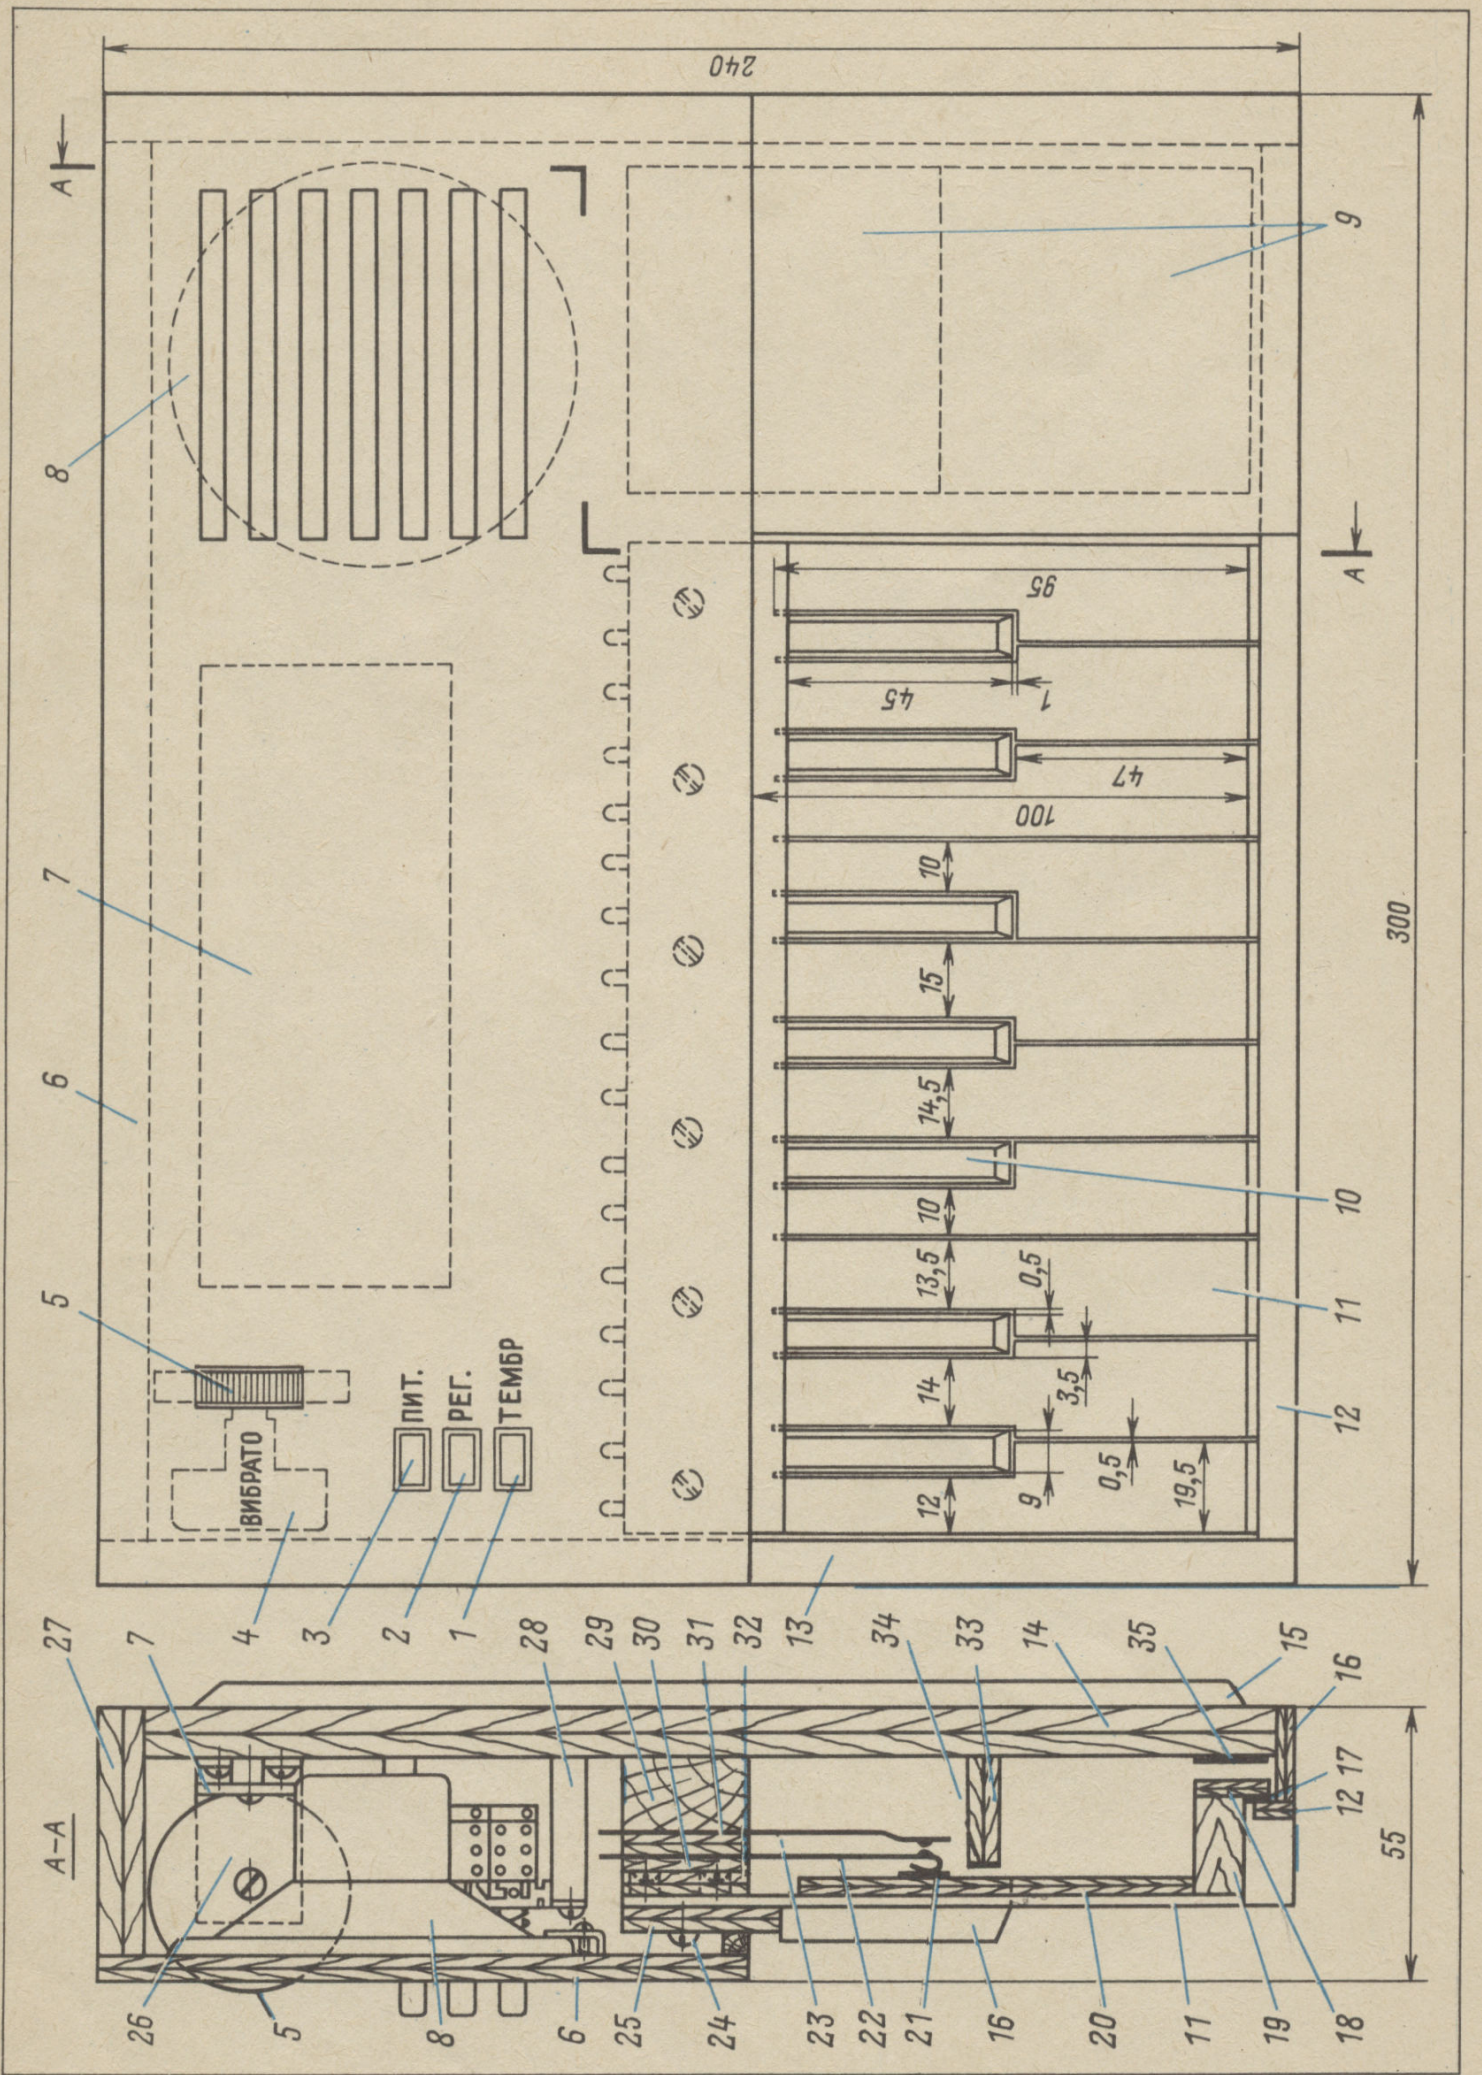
Конструкция клавиатуры и размещение деталей в корпусе «органа».
